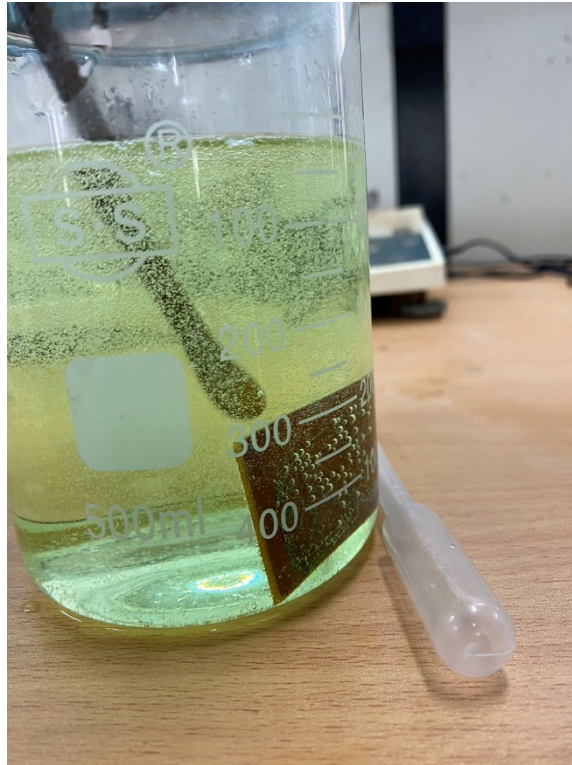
泡在鹽酸雙氧水混和液裡的 pcb
